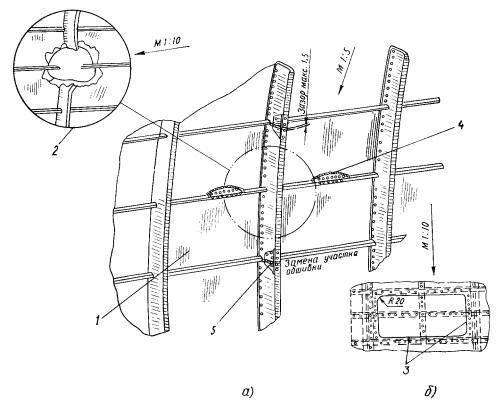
Устранение одновременного повреждения обшивки стрингера и шпангоута:
